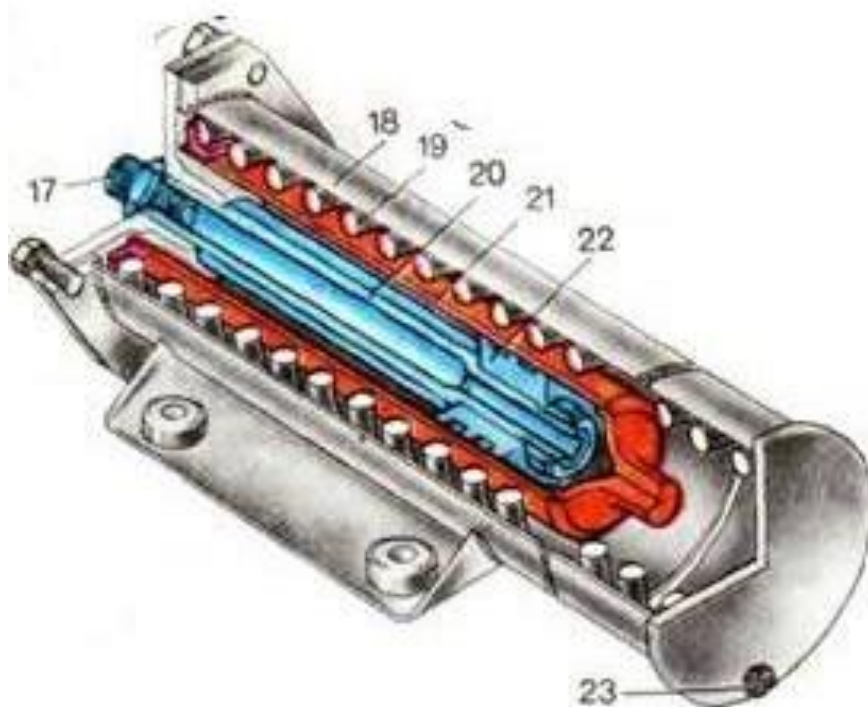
Гидроаккумулятор: 17— штуцер подсоединения маслопровода от ГСВ, 18 — кожух, 19 — пружина, 20 — шток, 21 — цилиндр, 22 — поршень, 23 — пробка
